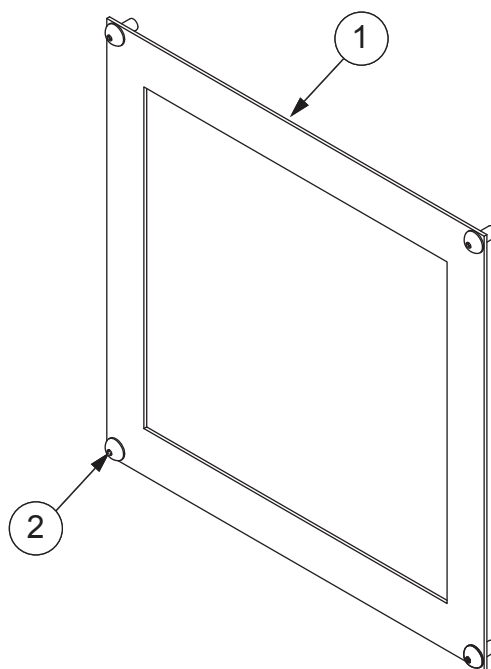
Plaque de montage pour le remplacement d'un relais SP_J6
